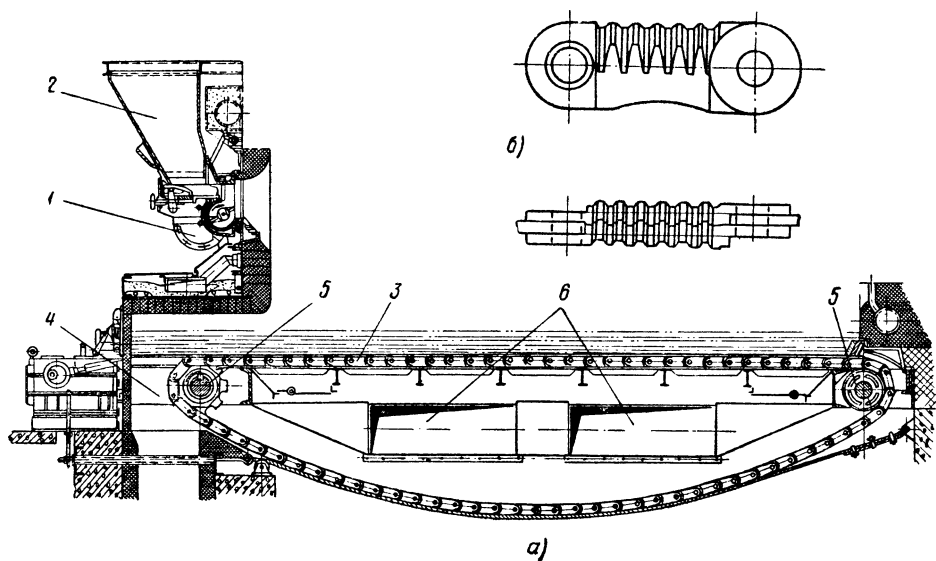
Топка с ленточной цепной решеткой обратного хода и забрасывателем топлива:
